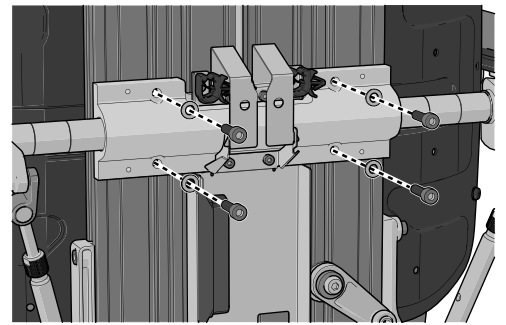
Die Armlehnen sind mit vier Schrauben befestigt.
